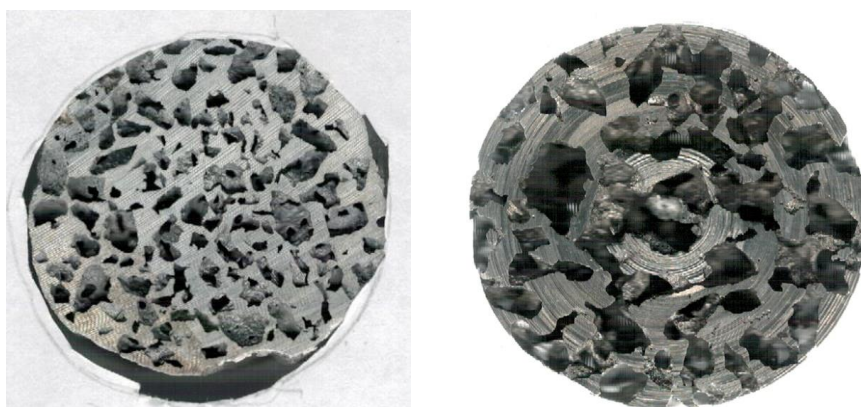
Пористые заготовки- преформы из матричного алюминиевого сплава с размером пор 1 и 5 мм
